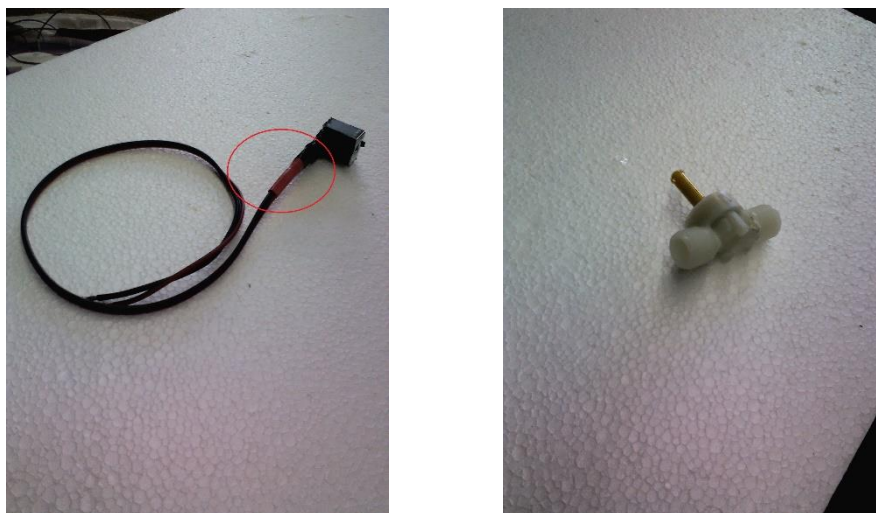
Bobina já impermeabilizada, e electroválvula, estes componentes operam em conjunto.
